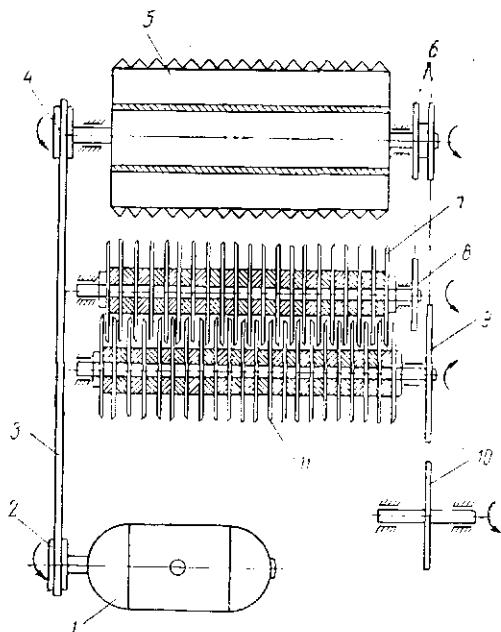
Кинематическая схема дискового пастигоготовителя:
